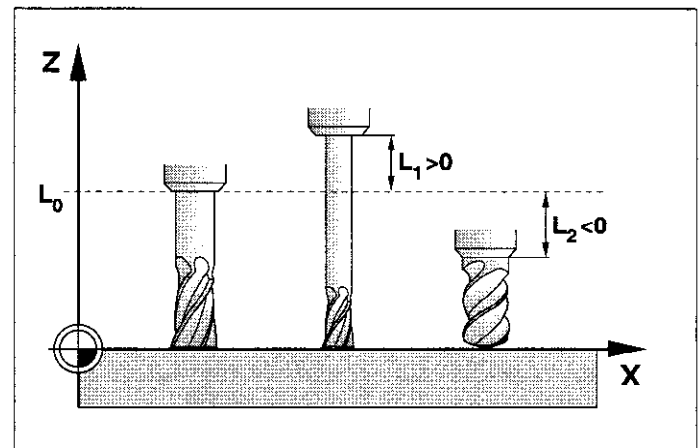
Werkzeug-Länge durch Längen-Unterschied zum Nullwerkzeug angeben
